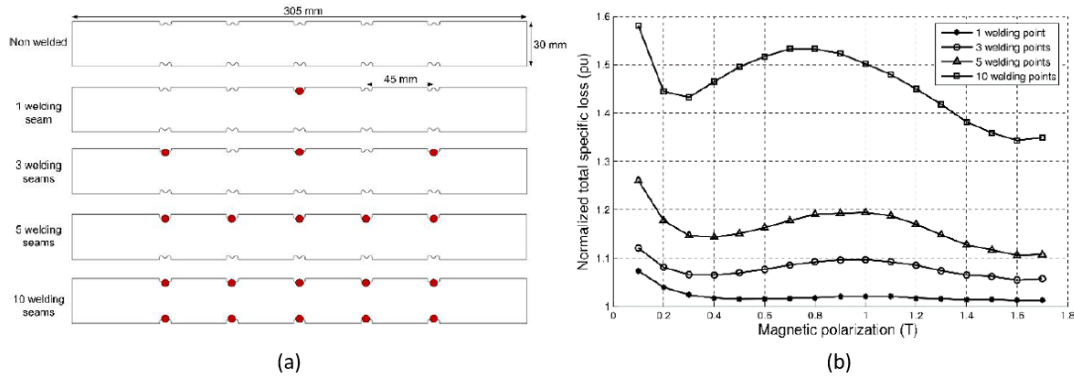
Echantillons soudés ou non (a) et effet de ces points de soudures sur les pertes Fer (b) [117]
